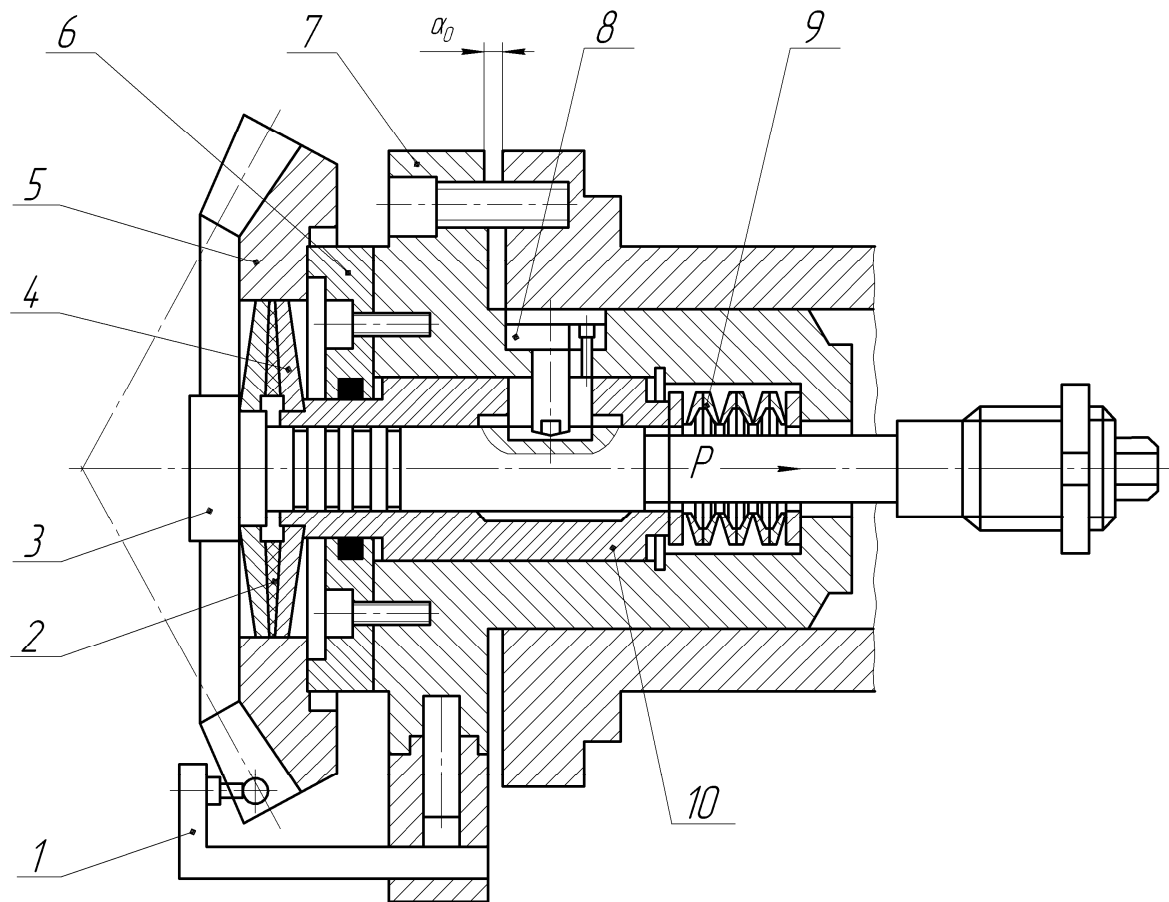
Будова затискного пристрою для обробки конічного колеса-диска: 1 – фіксатор; 2 – зовнішня мембрана тарілчастої форми; 3 – шток; 4 – внутрішня мембрана тарілчастої форми; 5 – оброблюване колесо; 6 – опорне колесо; 7 – оправка; 8 – шпонка; 9 – тарілчаста пружина; 10 – втулка
